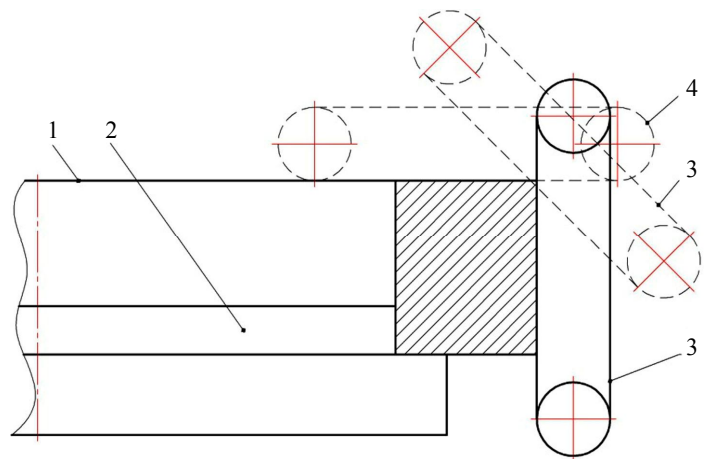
Схема ленточного шлифования при базировании бандажа на фундаменте или специальном стенде
